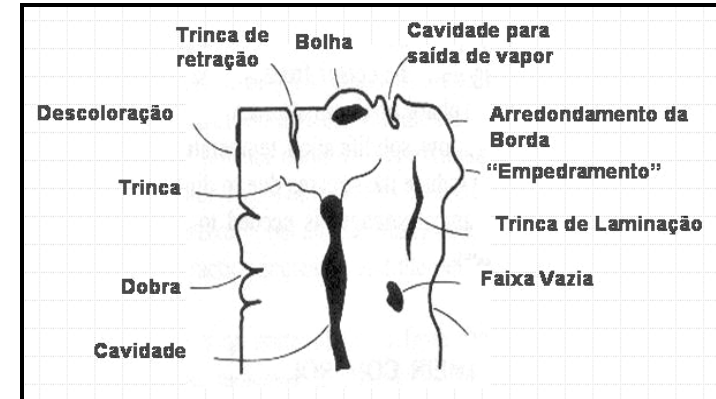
Ilustração de possíveis defeitos que ocorrem durante a moldagem por injeção, após a remoção do ligante.
